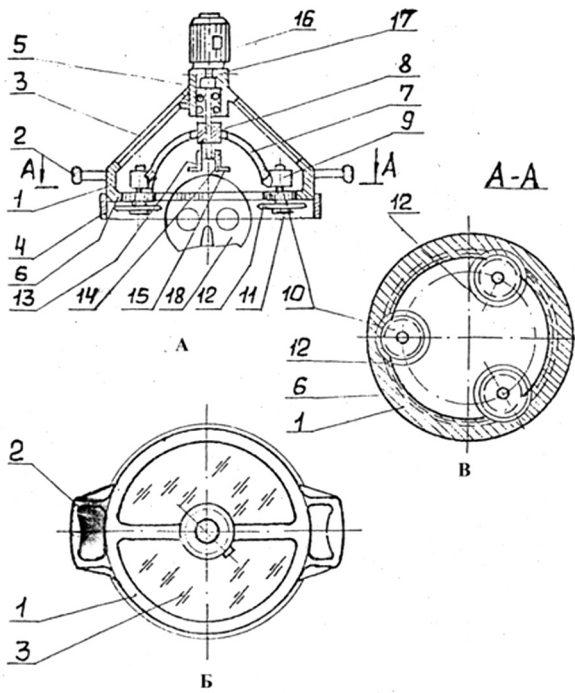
Схематическое изображение конструкции пилы медицинской: 1 – круговой каркас; 2 – боковые рукоятки; 3 – защитный контур; 4 – кольцевой щиток из оргстекла; 5 – муфта; 6 – центральная неподвижная шестерня; 7 – вращательный фиксатор; 8 – резьбовая нарезка с муфтой; 9 – подшипниковые узлы; 10 – шестеренки-сателлиты; 11 – ось; 12 – двигательные резательные элементы; 13 – вертикальный ограничитель высоты; 14 – втулка с резьбой; 15 – плоский фланец; 16 – электродвигатель; 17 – вал вращательного фиксатора; 18 – череп, предназначенный для кругового распиливания.
